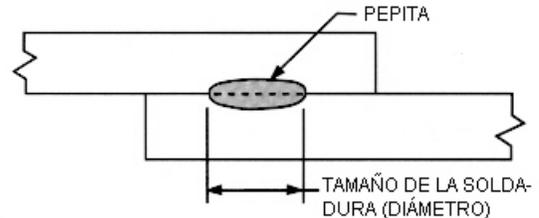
Tamaño de la soldadura por puntos o por costura
